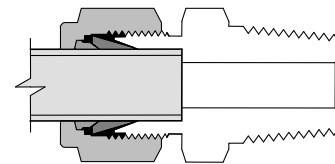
Asegúrese que el adaptador de tubo está apoyado firmemente sobre el hombro del cuerpo del racor de tubo
